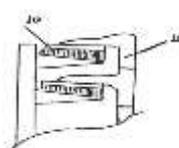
Вид сбоку хлопкоуборочной машины с горизонтальным шпинделем (кинематическая схема)
